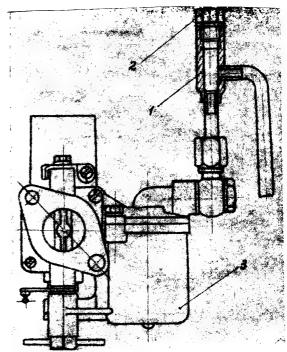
Заливная трубка для пускового бензина: I— заливная трубка; 2— пробка заливной трубки; 3— поплавковая камера карбюратора
